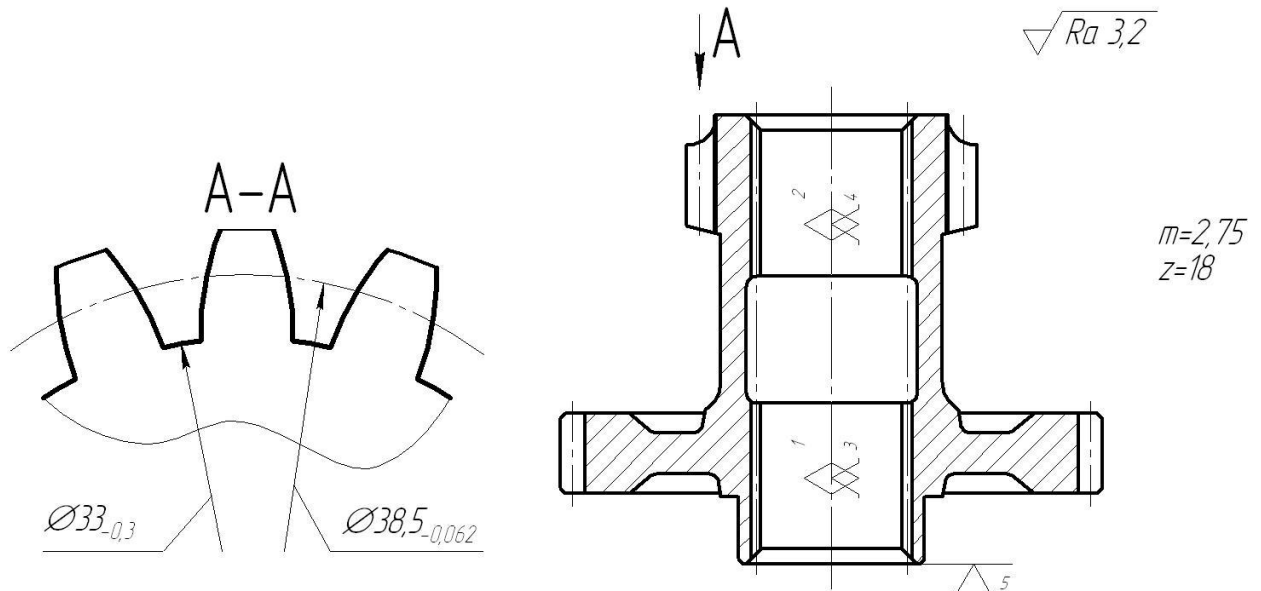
Эскиз операции 050 Зубофрезерная
